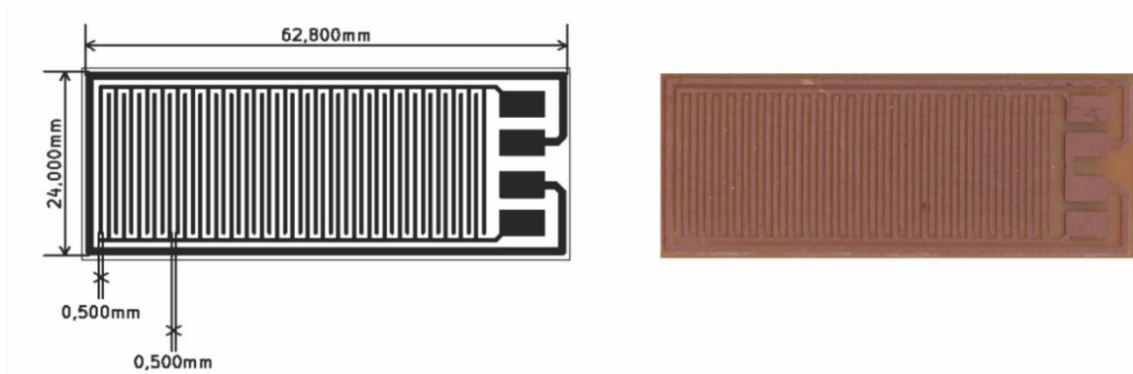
Sensor S500 $\mu\text{m}$ : dimensões desejadas e sensor obtido pela usinagem em mesa de corte Router CNC.
